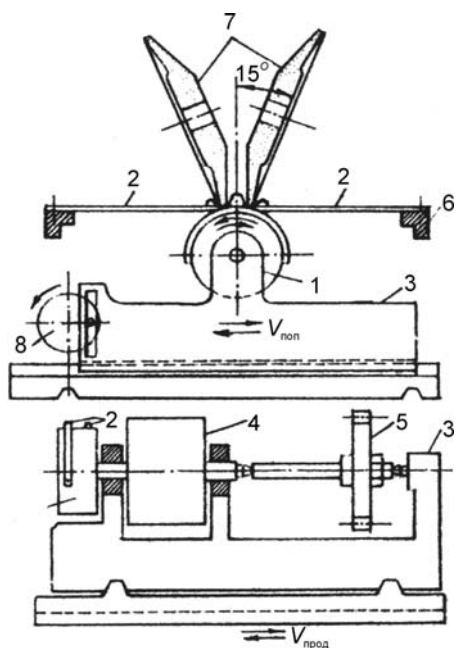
Схема работы зубо-шлифовального станка 5851 МААГ.
